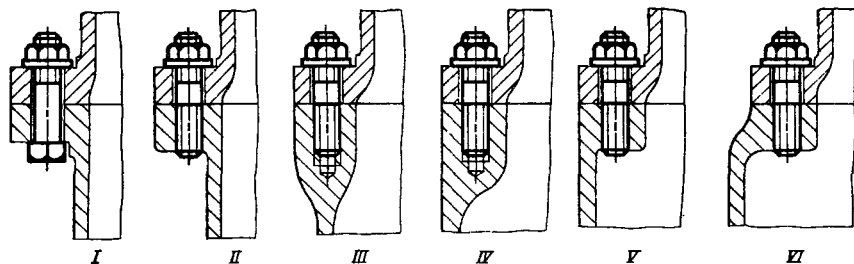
Формоизменение корпусной детали, допускаемое применением шпилек и свертных болтов
